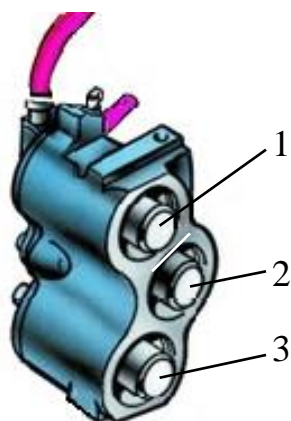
Рабочий цилиндр тормозного механизма переднего колеса полноприводного автомобиля ВАЗ-21213: 1 – поршень первого контура; 2 и 3 – поршни второго контура
